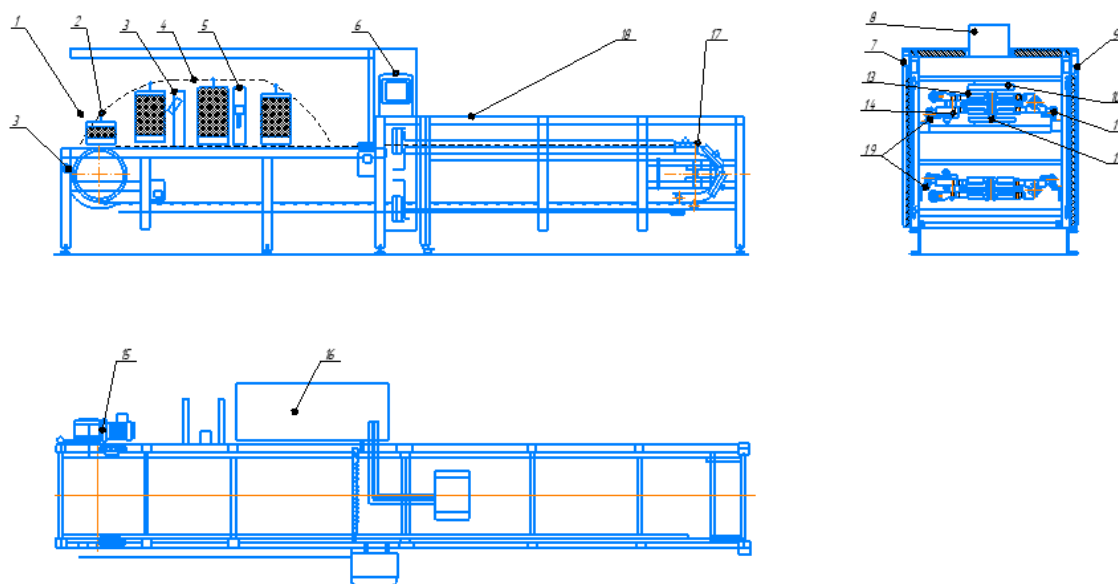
Общий вид вафельной печи: 1 – разгрузочно-загрузочная камера; 2 – вафельная форма; 3 – устройство пневмосдува; 4 – механизм раскрытия форм; 5 – дозатор теста; 6 – дисплей управления; 7 – боковая дверь; 8 – патрубок отвода газов; 9 – боковая дверь; 10 – верхний плоский индуктор; 11 – ходовое колесо; 12 – нижний плоский индуктор; 13 – верхняя часть вафельных формы; 14 – нижняя часть вафельной формы; 15 – электродвигатель; 16 – электрический шкаф; 17 – бесконечная цепь вафельных форм; 18 – корпус; 19 – направляющие
